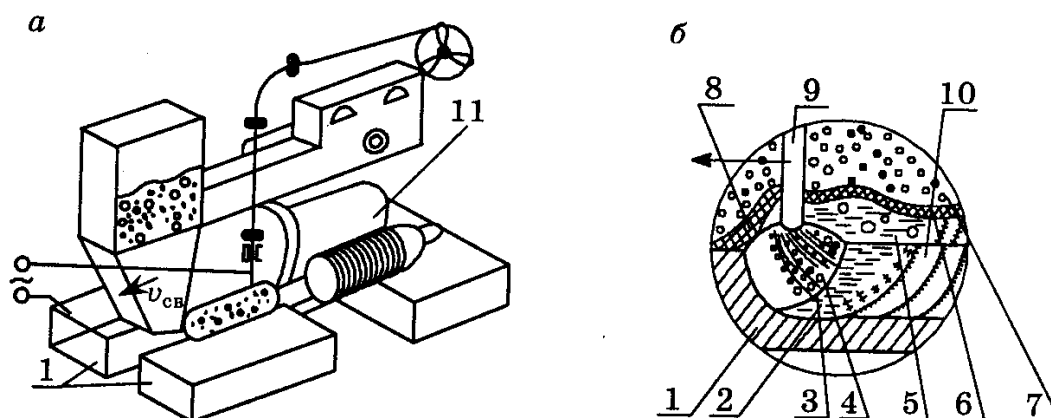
Схемы процесса сварки (а) и электрической дуги (б) под флюсом
